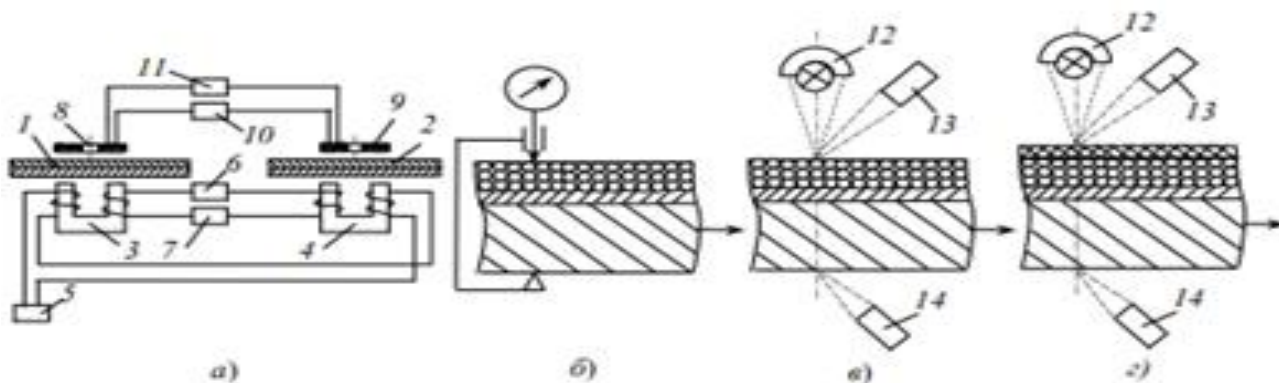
Схема непрерывного контроля качества металлофторопластового ленточного материала в технологическом потоке ее изготовления:
